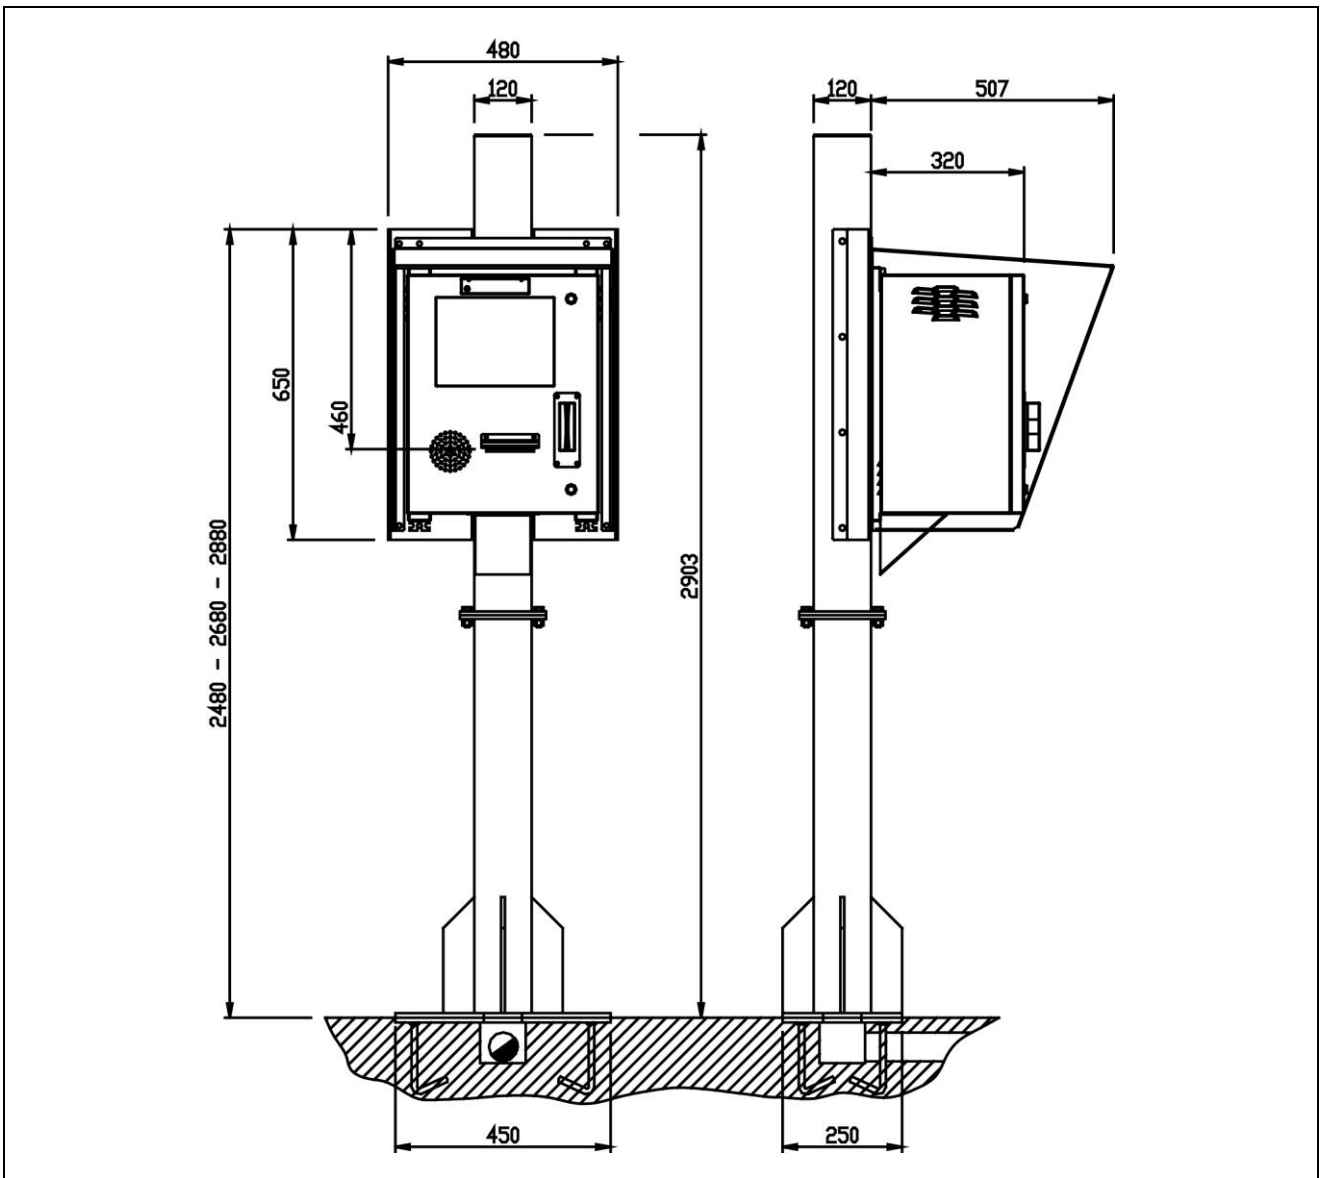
Gesamtabmessungen des Terminals mit Sockel
